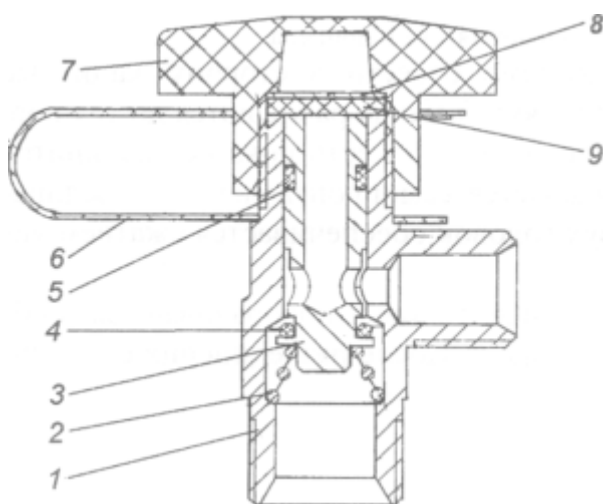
Кран экстренного растормаживания: 1- корпус; 2 - пружина; 3 - толкатель; 4, 5 - кольцо уплотнительное; 6 - лента; 7 - гайка-барашек; 8 - шайба; 9 - прокладка
